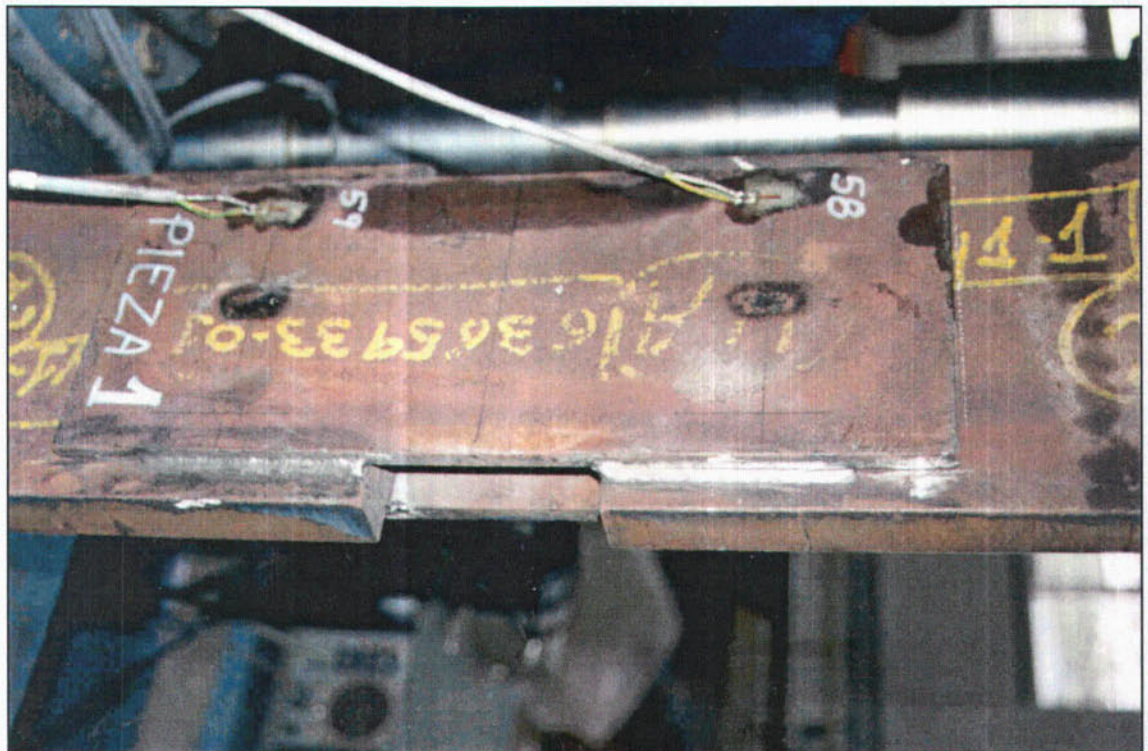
Detalle de rotura de soldadura por el plano de garganta en la probeta 2T.
